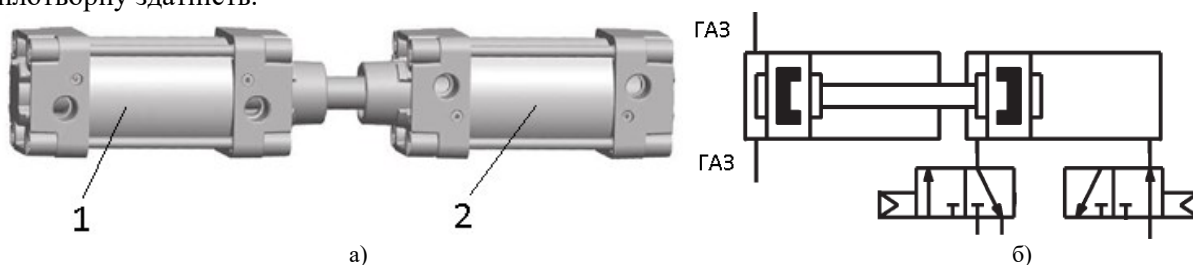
Типовий опозитний пневмоциліндр (а) та пневматична схема пробовідбірника – дозатора (б)
